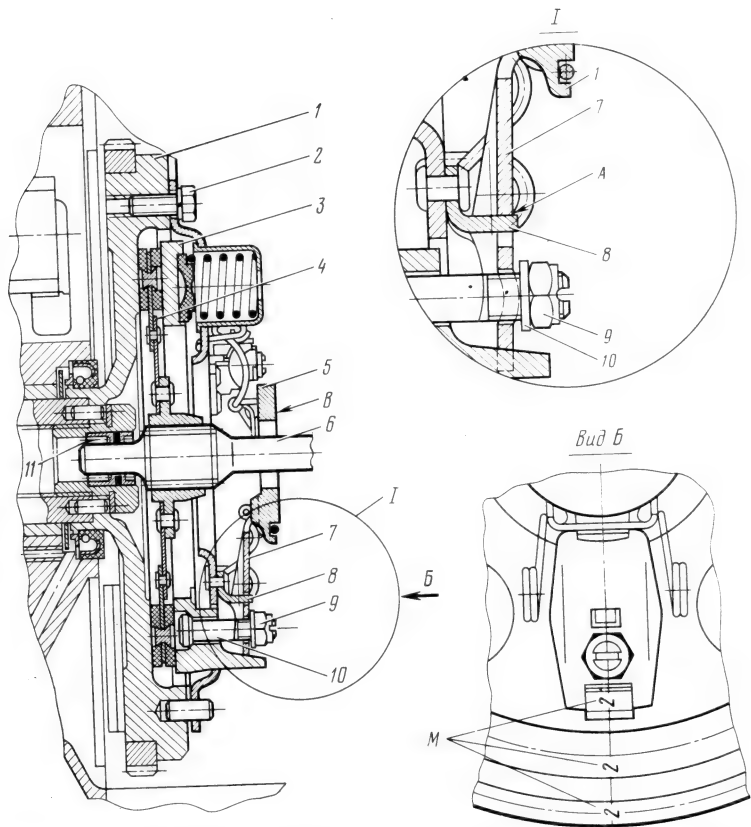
Установка ведомого диска сцепления с помощью оправки:
